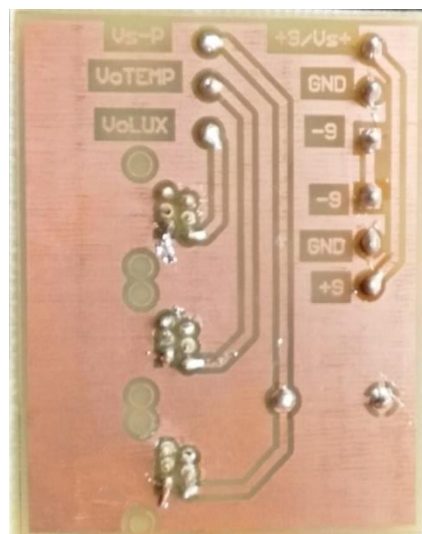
Vista cara inferior PCB conexión Sonda-NXT
